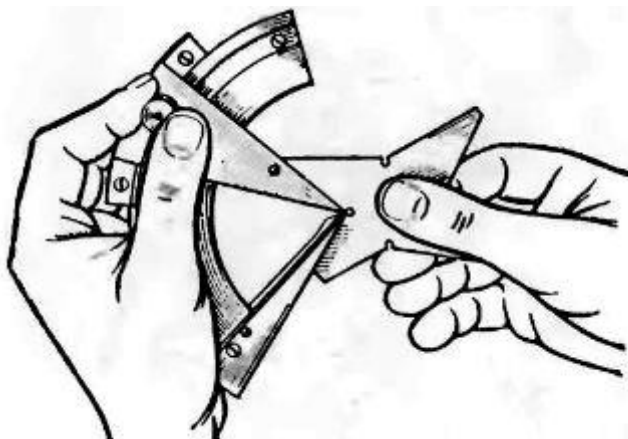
Установка угломера относительно внутреннего угла незакрепленной детали при помощи микроподачи
